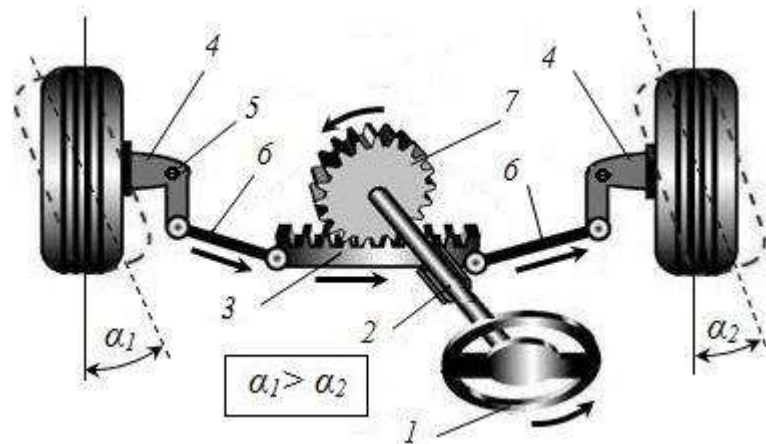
Принципова схема рульового керування з рейковим механізмом:
